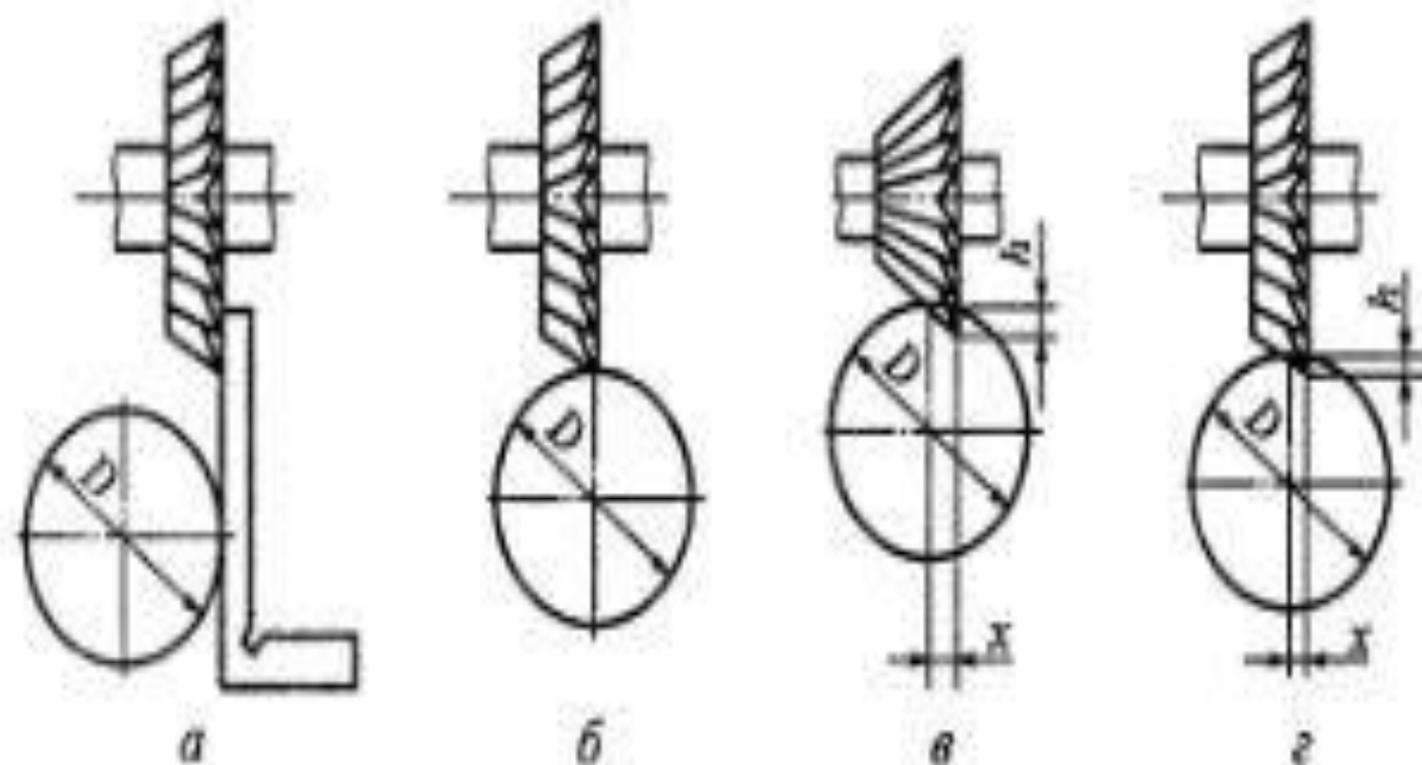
Схема установок фрез при фрезеровании канавок режущих инструментов:
